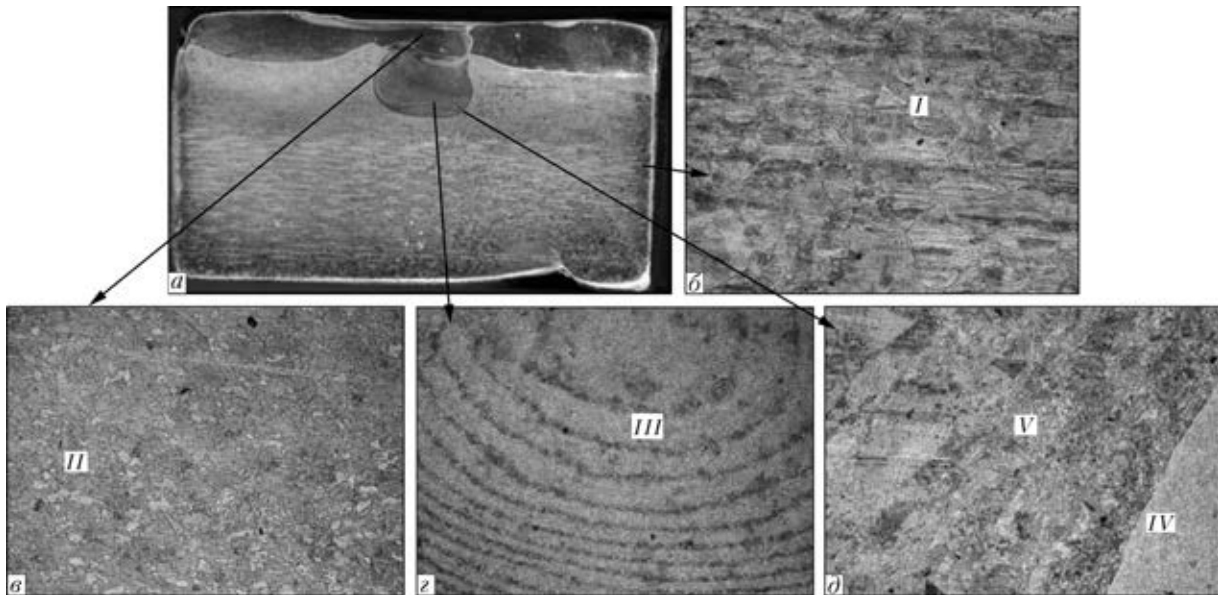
Структура металла сварного соединения (поперечный разрез), полученного при СТП медных пластин: *a* – общий вид; *b* – основной металл; *c* – металл верхней пластины; *d* – ядро соединения; *e* – зона термомеханического влияния; *a* – $\times 3$; *b-d* – $\times 100$
